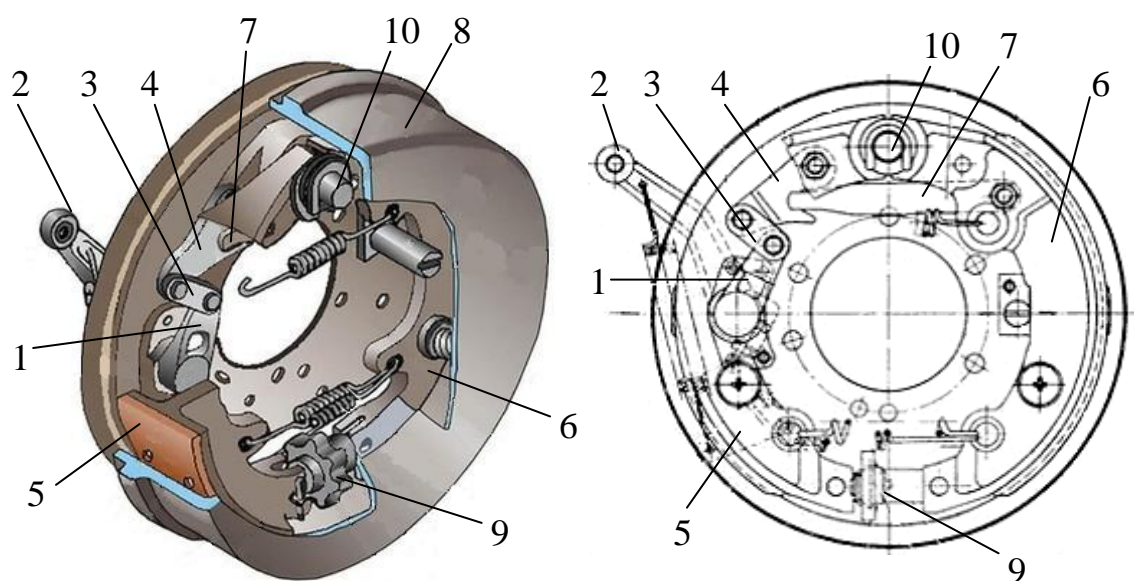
Трансмиссионный барабанный тормозной механизм стояночного тормоза грузового автомобиля УРАЛ: 1 – рычаг; 2 – рычаг привода разжимного механизма; 3 – серьга; 4 – разжимной рычаг; 5 и 6 – тормозные колодки; 7 – штанга; 8 – тормозной барабан, 9 – регулировочное устройство; 10 – опорный палец
